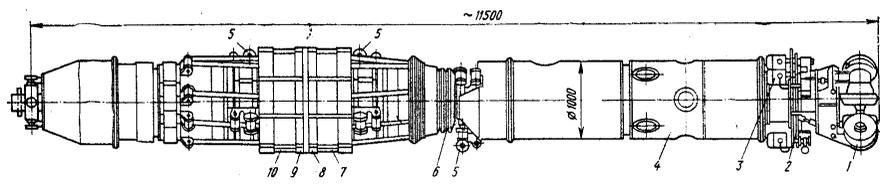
Внутритрубная машина для сборки и сварки магистральных трубопроводов большого диаметра
